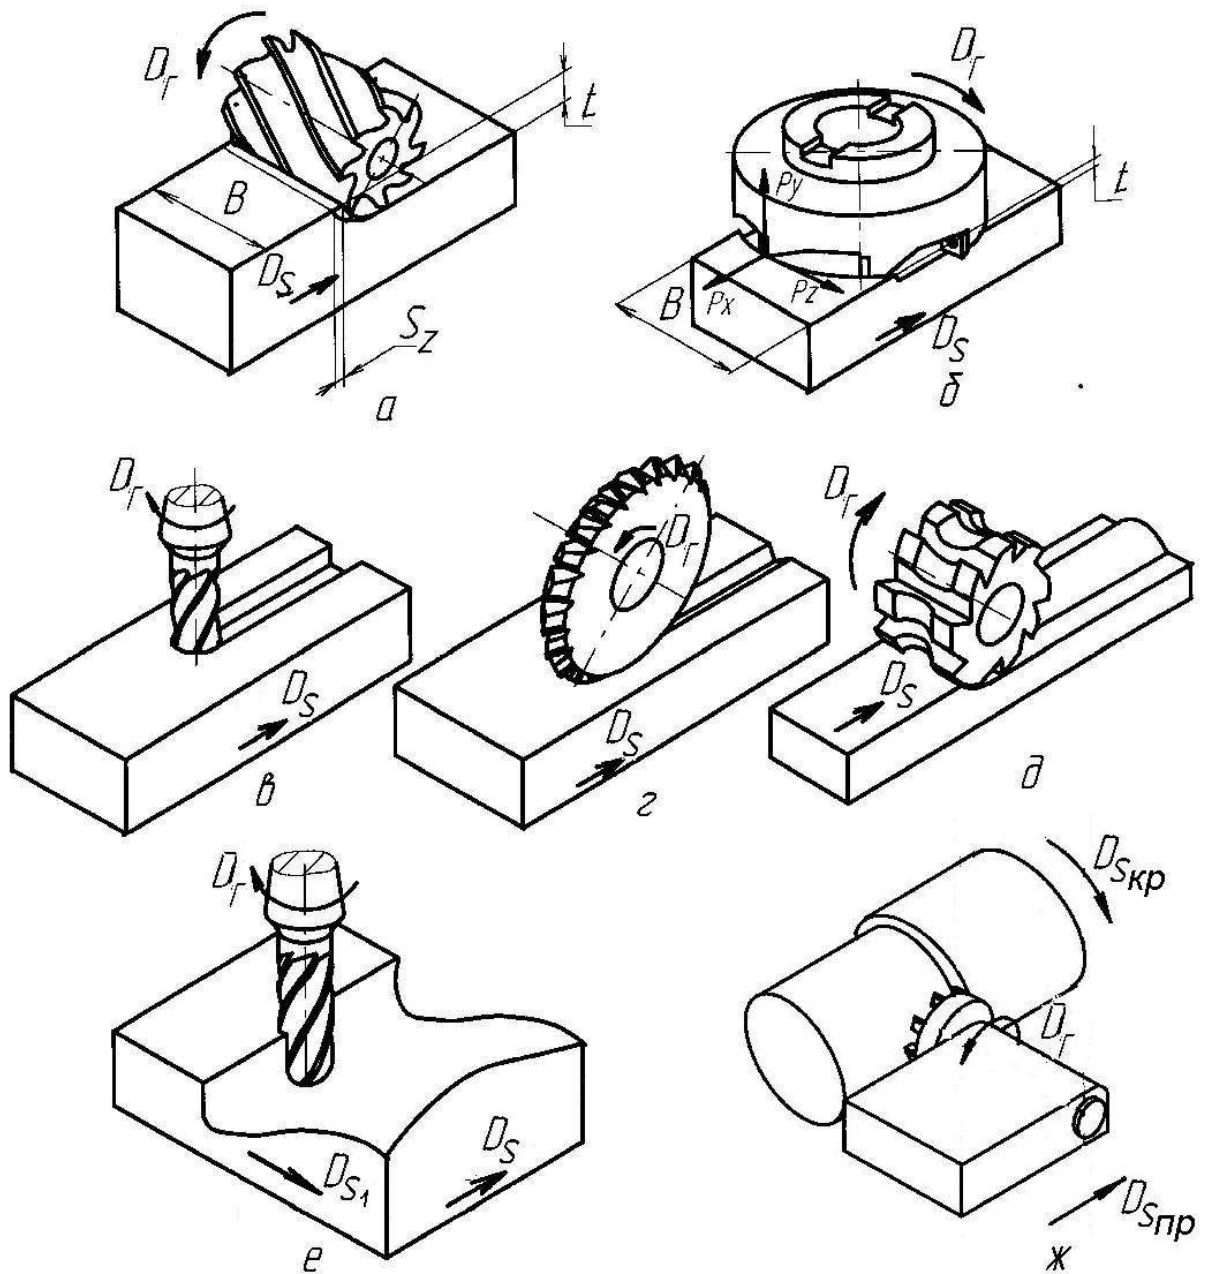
, Различные схемы обработки поверхностей фрезерованием: а,б- плоскости цилиндрической и торцевой фрезой, в,г- паза концевой и дисковой фрезой, д - профильной поверхности фасонной фрезой, е - поверхности двойной кривизны концевой фрезой при перемещении ее по сложной траектории, ж- фрезерование вращающейся заготовки (ротационное фрезерование)
